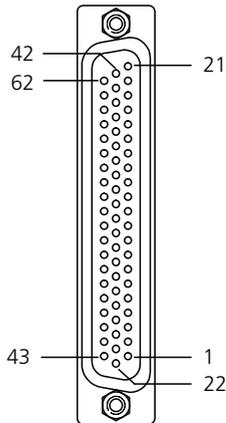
Frontstecker des PB4350DAC1 D/A Module (Ansicht von Steckseite)
